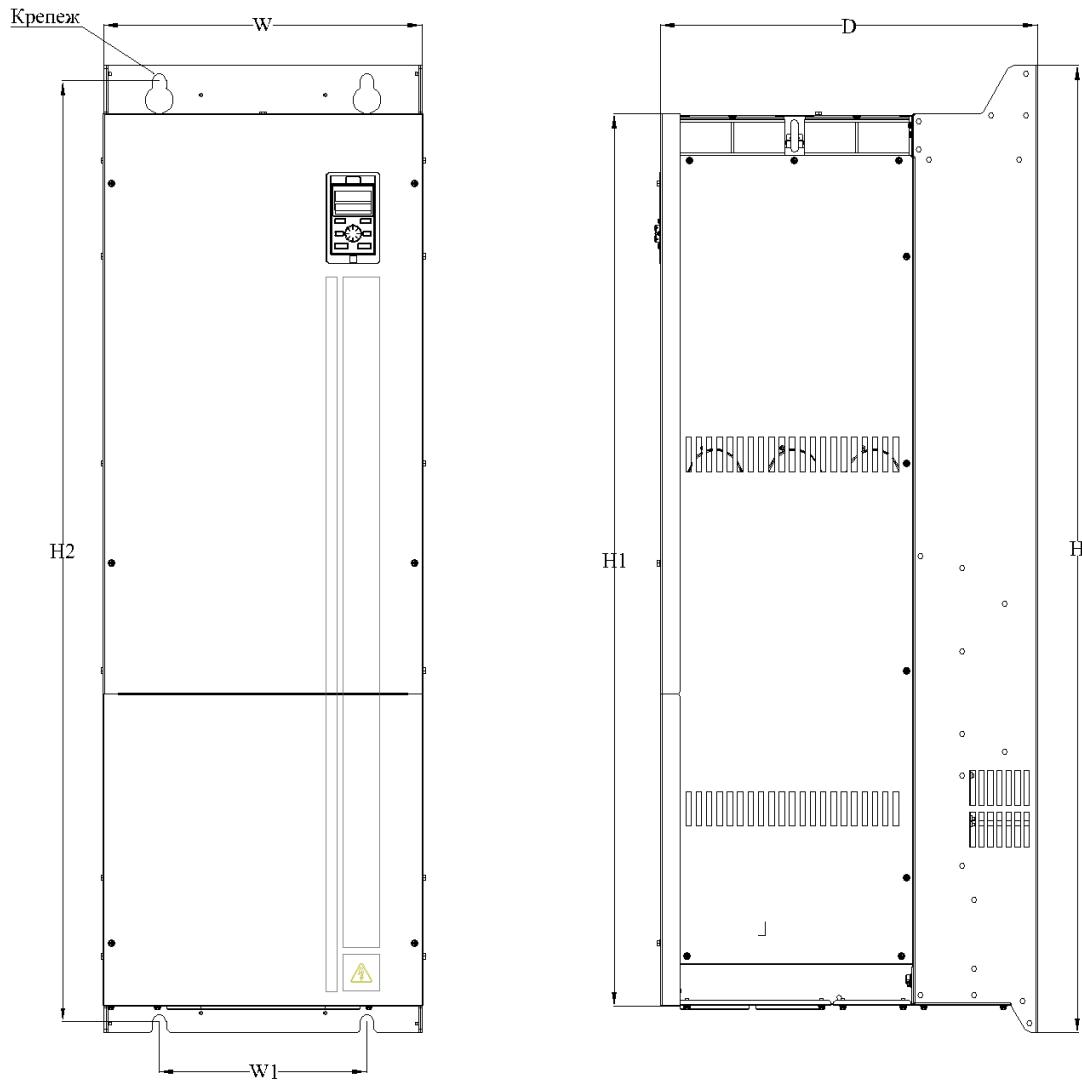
Чертеж преобразователя частоты типоразмер 11
